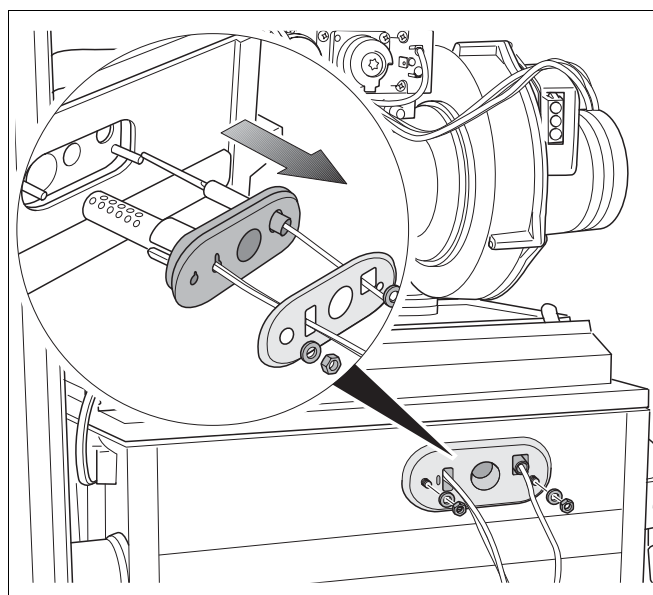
Demontați electrodul de ionizare și electrodul de aprindere
